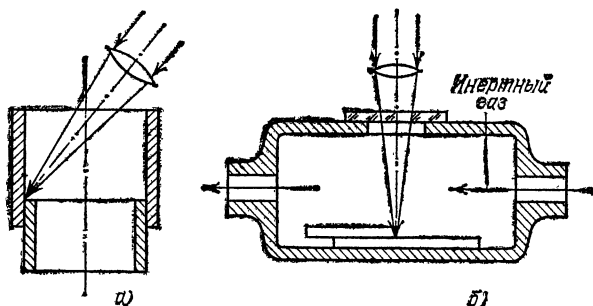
а) Лазерная сварка в труднодоступном месте. б) Лазерная сварка в камере, заполненной инертным газом.
